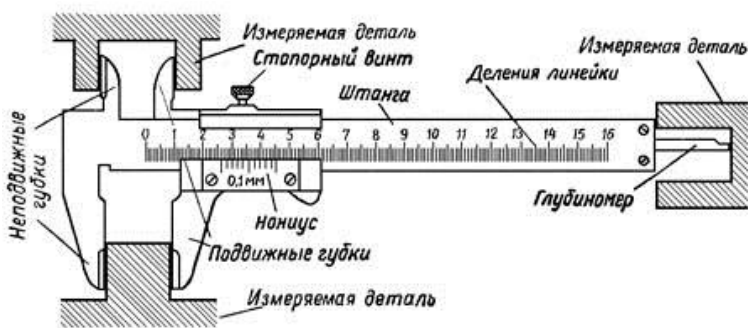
Штангенциркуль ШЦ-I. Основные элементы
